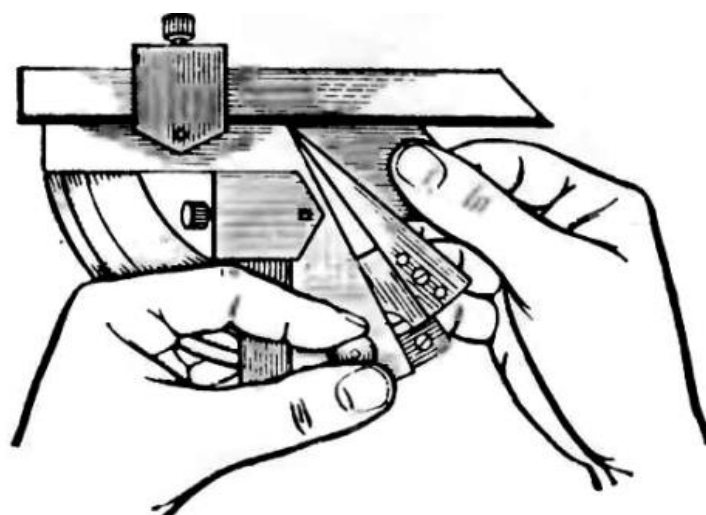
Установка угломера относительно наружного угла незакрепленной детали при помощи микроподачи
